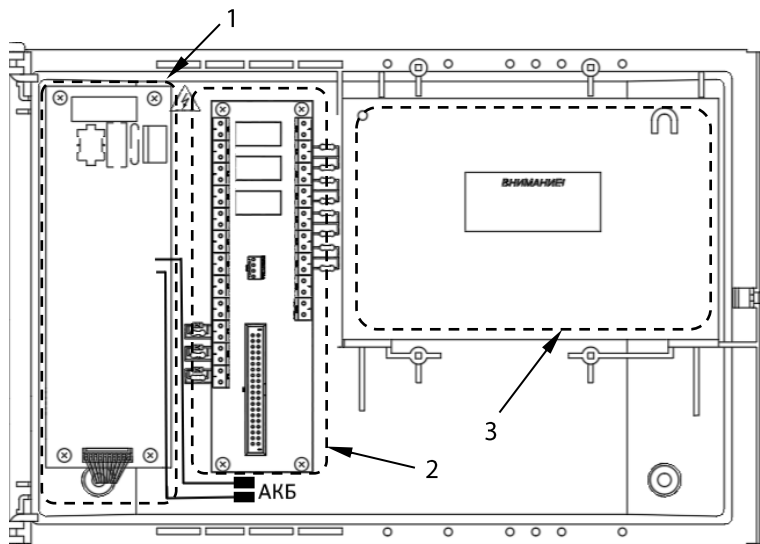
Компоновка плат в корпусе ЛЕОН2-ППК.
